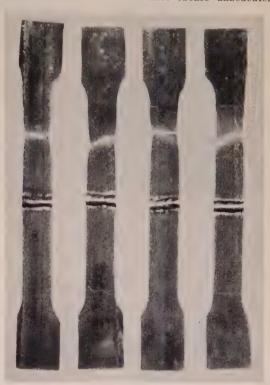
Lage der Bruchstelle bei den 25 mm breiten Proben mit aufgelegter Quernaht
